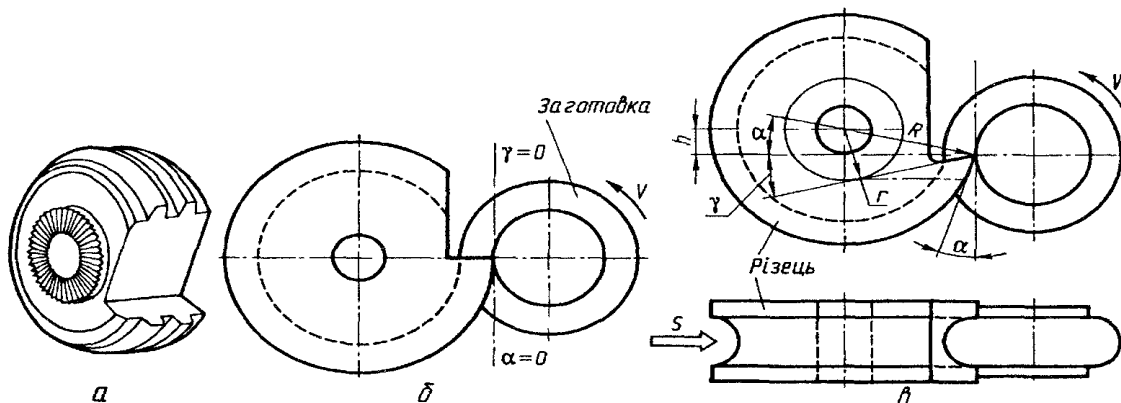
Дисковий фасонний різець: а - загальний вигляд; б - установлений по центру заготовки; в - установлений вище від центра заготовки
